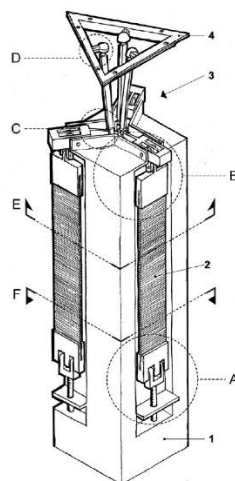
Esboço de um protótipo de seguimento solar passivo - SEGSOL. Fonte: [12]
